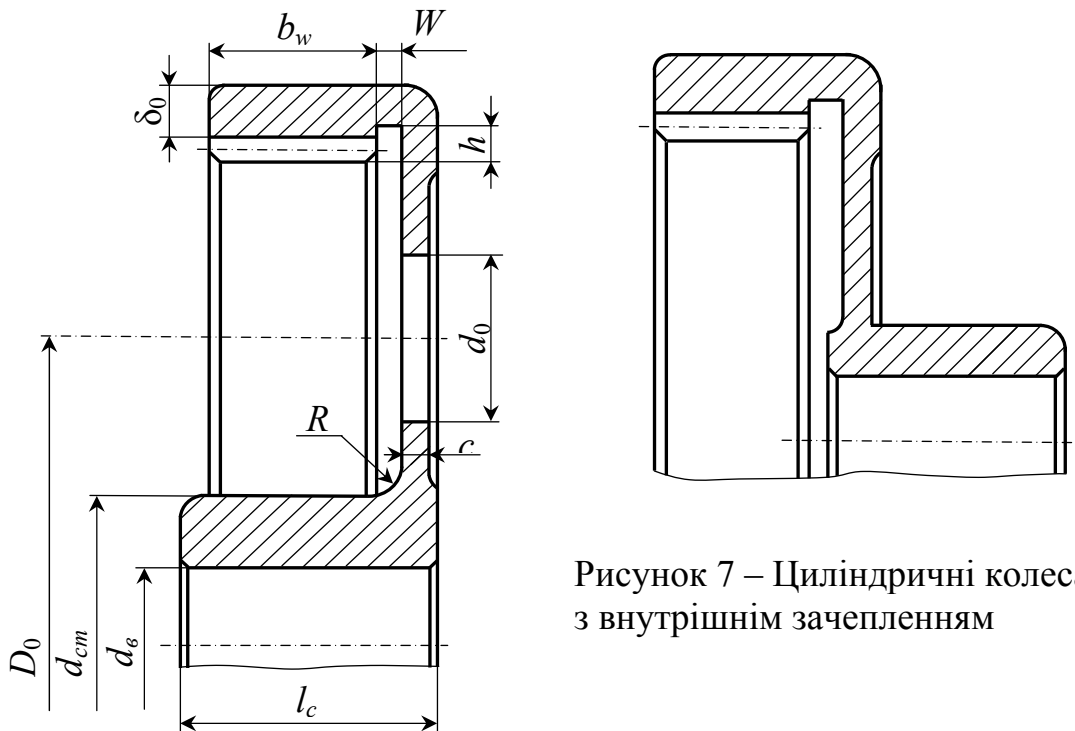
Циліндричні колеса з внутрішнім зачепленням
